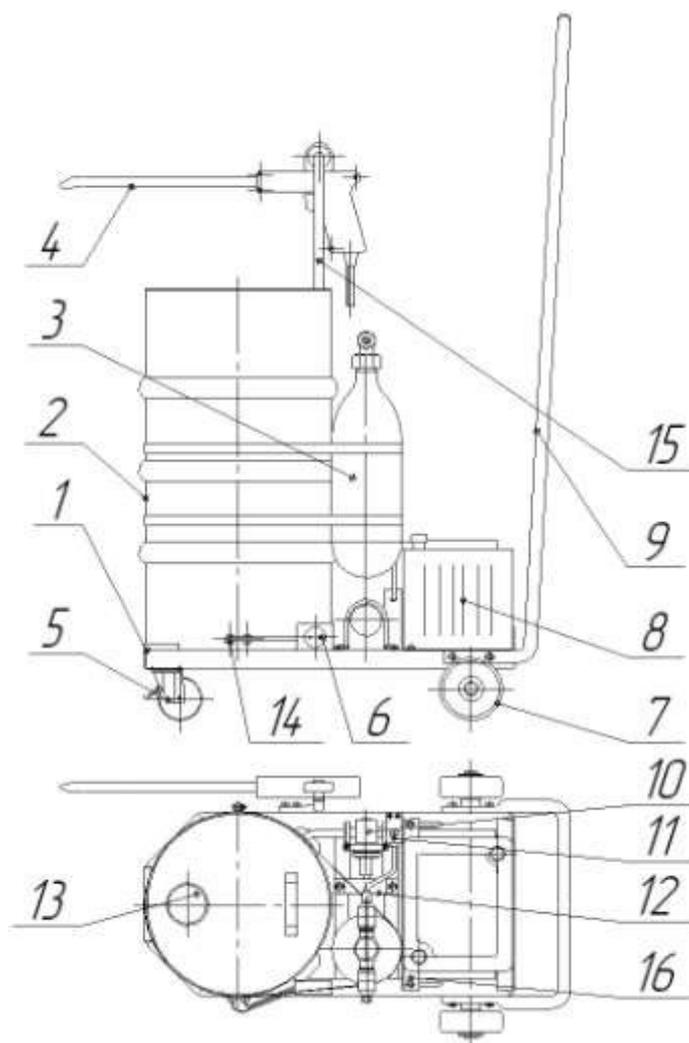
Устройство конструкции разрабатываемого устройства для выдачи консистентных смазок
